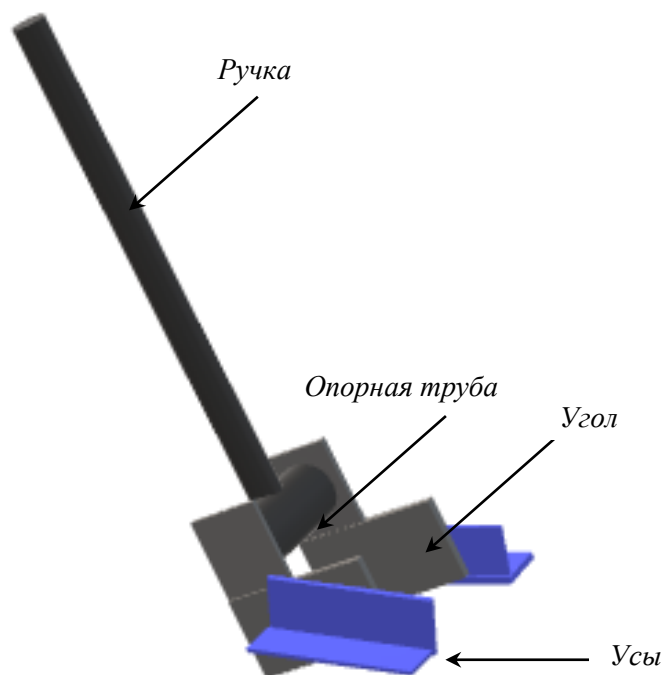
Внешний вид «Универсального гвоздодера»
